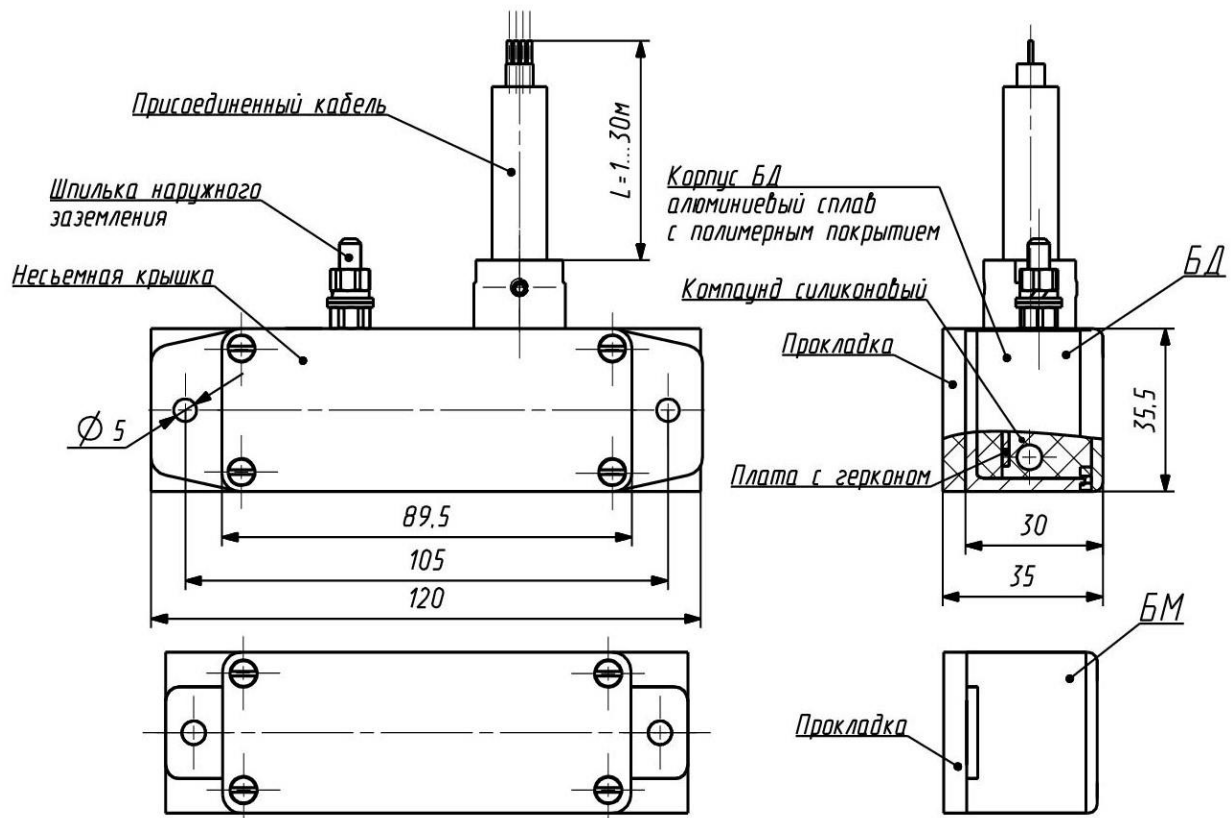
Габаритный чертёж извещателя ЕхИО102-2/12
